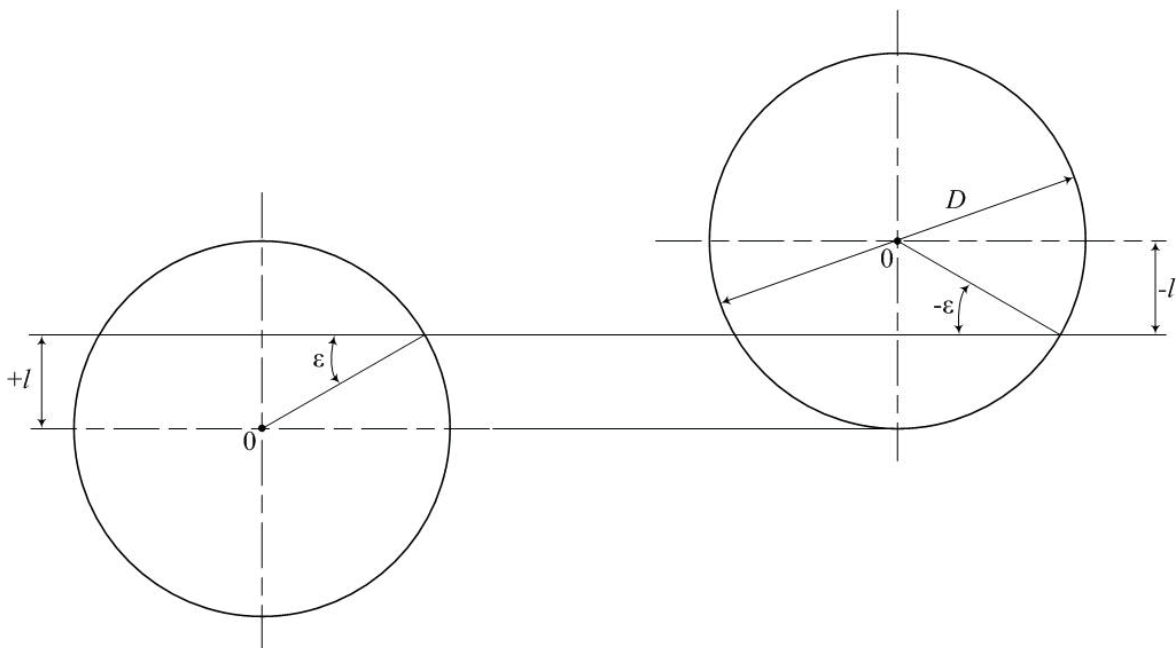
Условия первоначального контакта зуба фрезы и обрабатываемой поверхности заготовки
